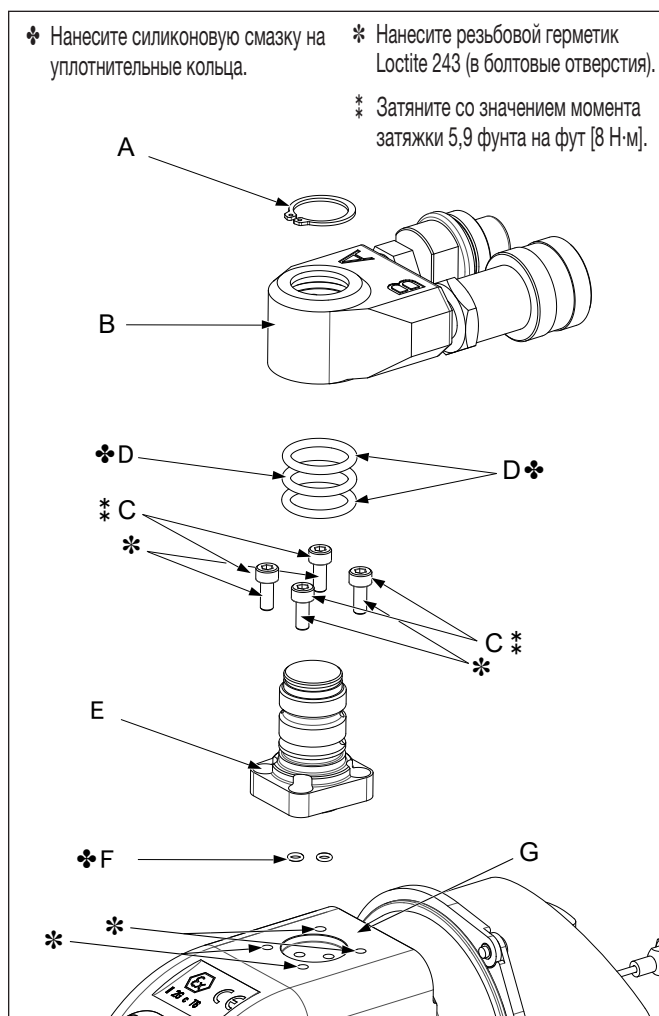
Стойка вертлюга и вертлюжное соединение в сборе
